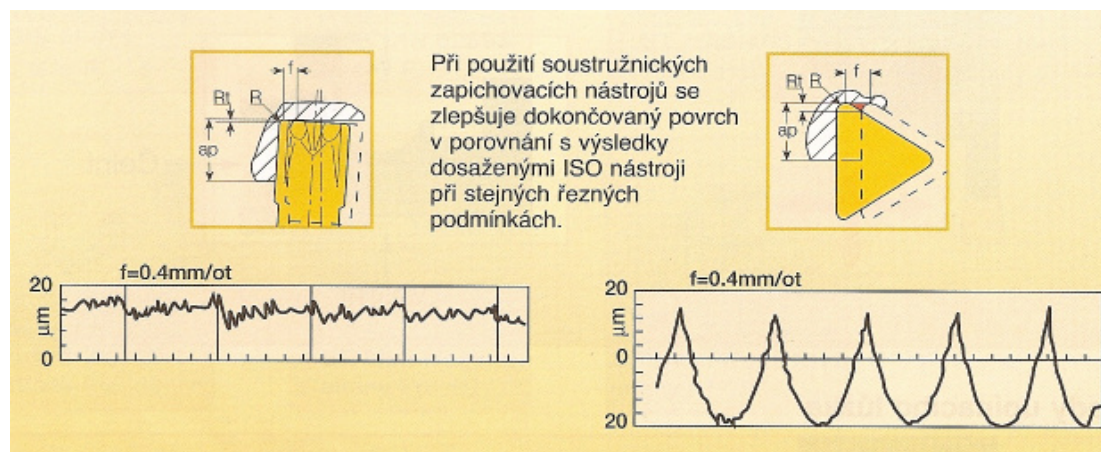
Příklad použití soustružnického zapichovacího systému ^[6]
